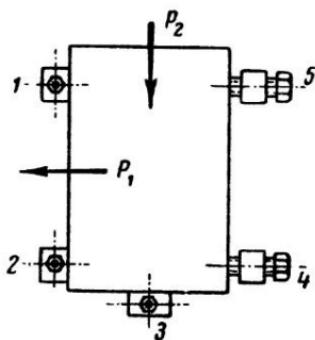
Схема крепления деталей и приспособлений к столу строгального станка: 1, 2, 3 — упоры; 4, 5 — прижимные болты; P_1 — направление подачи стола; P_2 — направление строгания.
